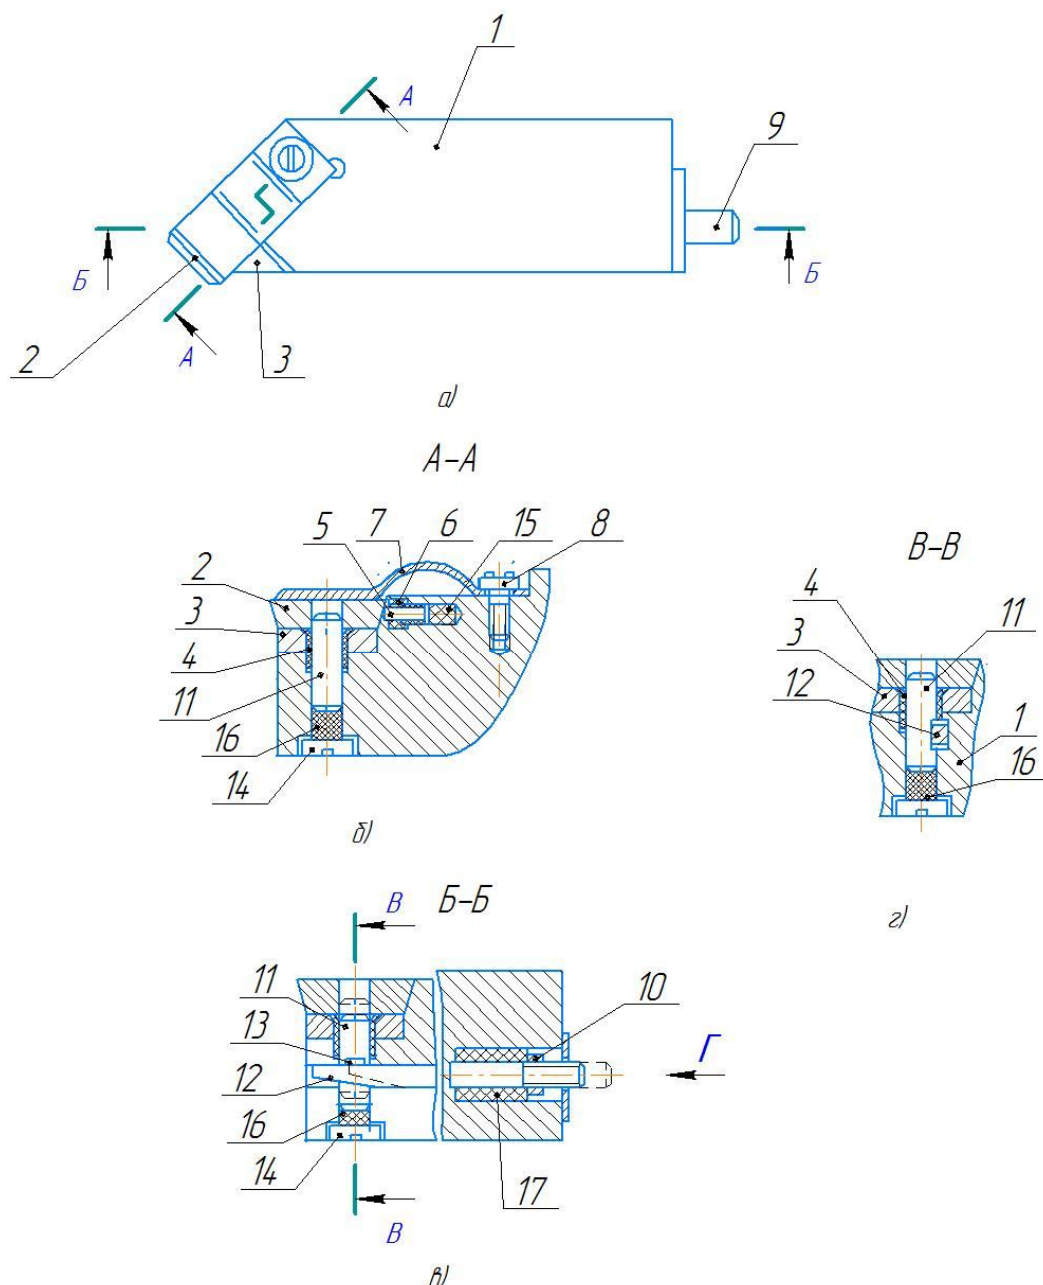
Демпфирующий сборный резец с автоматической сменой режущей пластины
